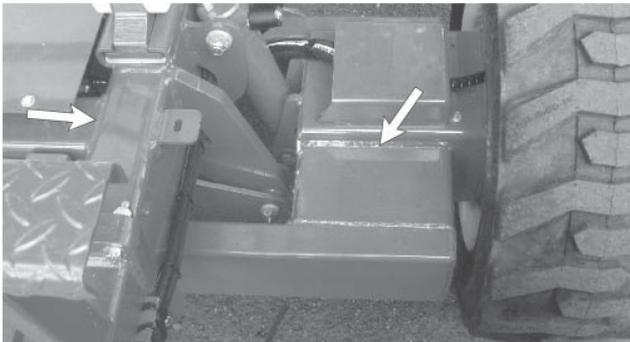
Strukturelle Schäden und Schweißnähte
